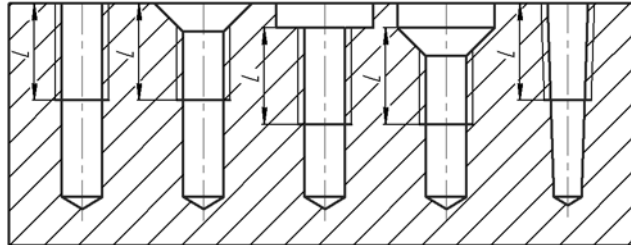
Начальная граница резьбы для разных типов отверстий
